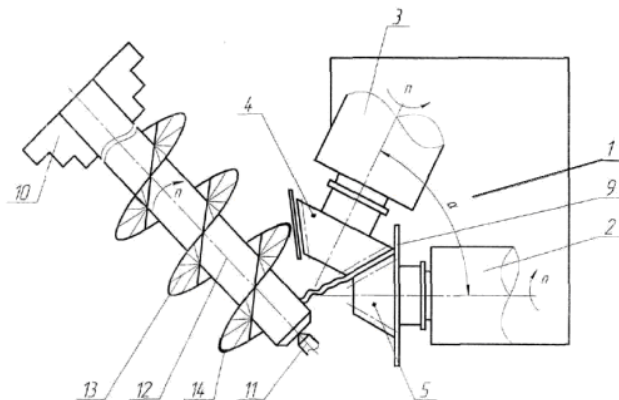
Обкатний верстат для виготовлення гвинтових гофрованих заготовок
